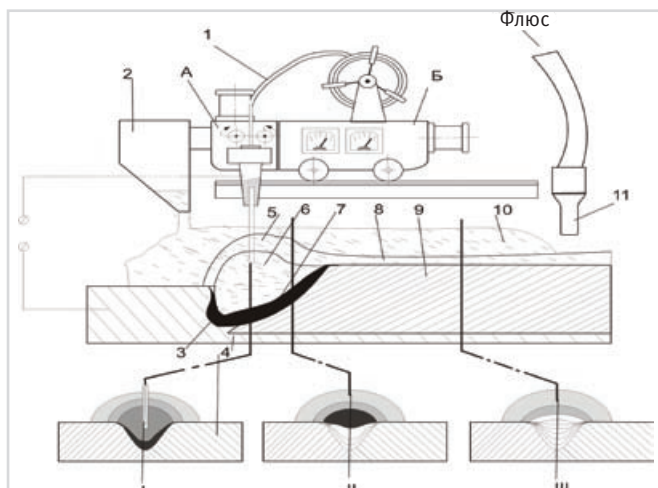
Схема сварки под флюсом: А — сварочная головка; Б — механизм перемещения; I, II, III — поперечные сечения в различных зонах шва
